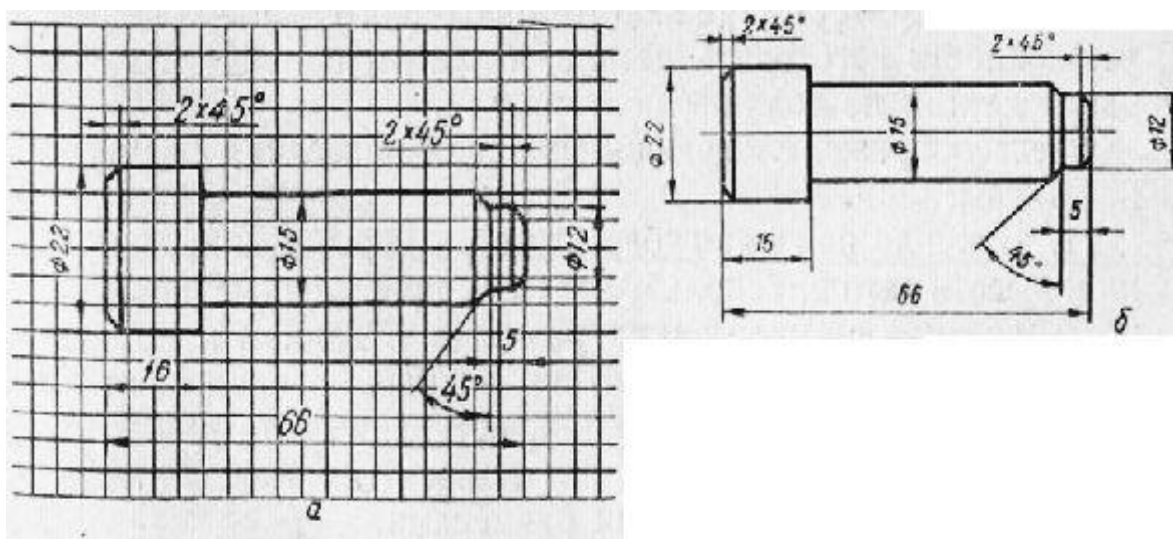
Эскиз детали (а) и её чертёж (б)
